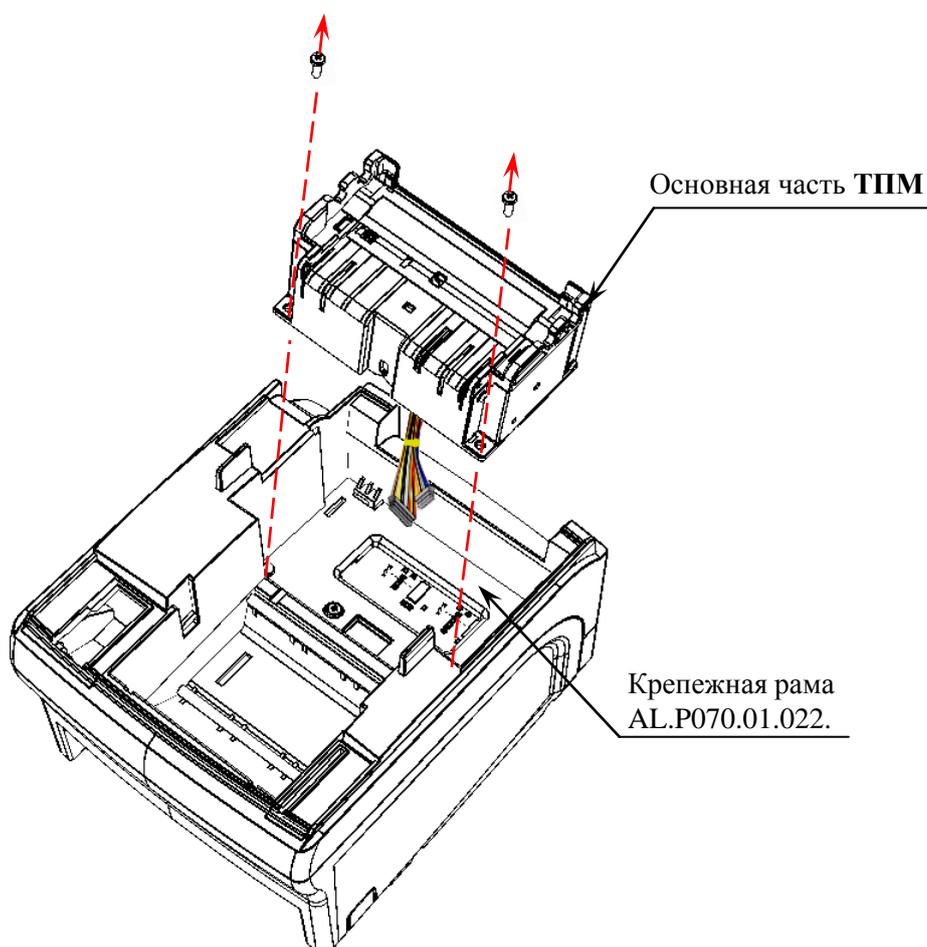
Установка ТПМ (крышка изделия условно не показана).
